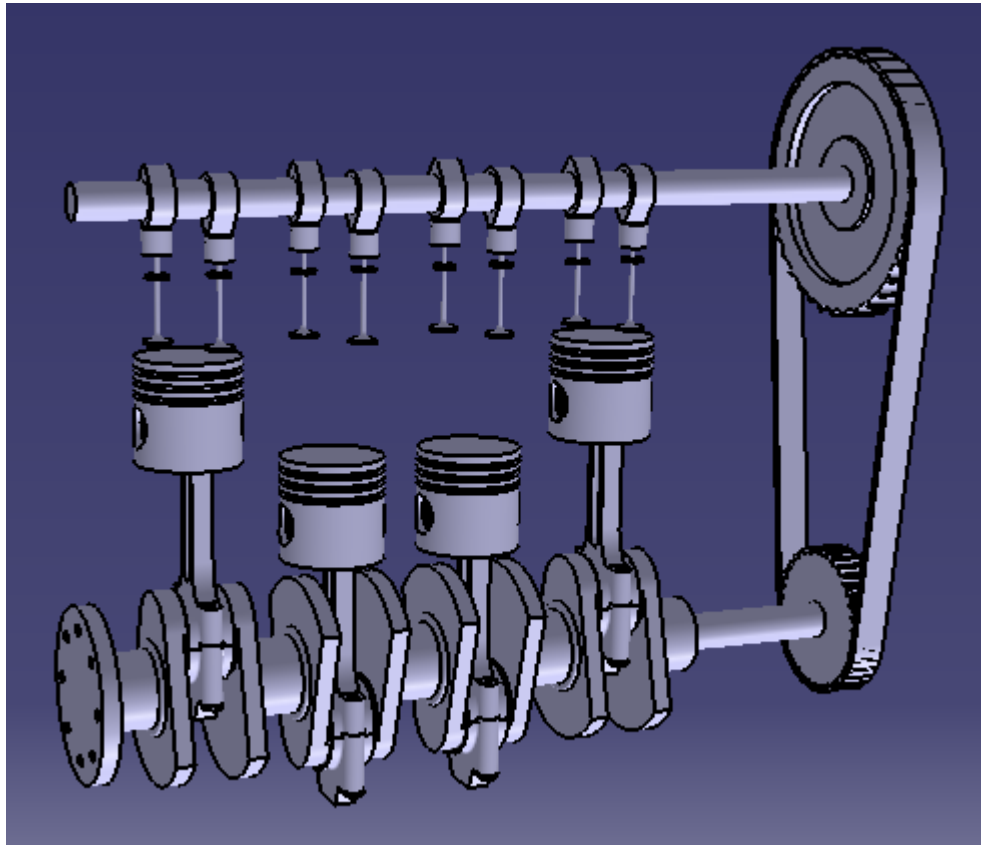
Aspecto final del ensamblado sin el bloque motor.
